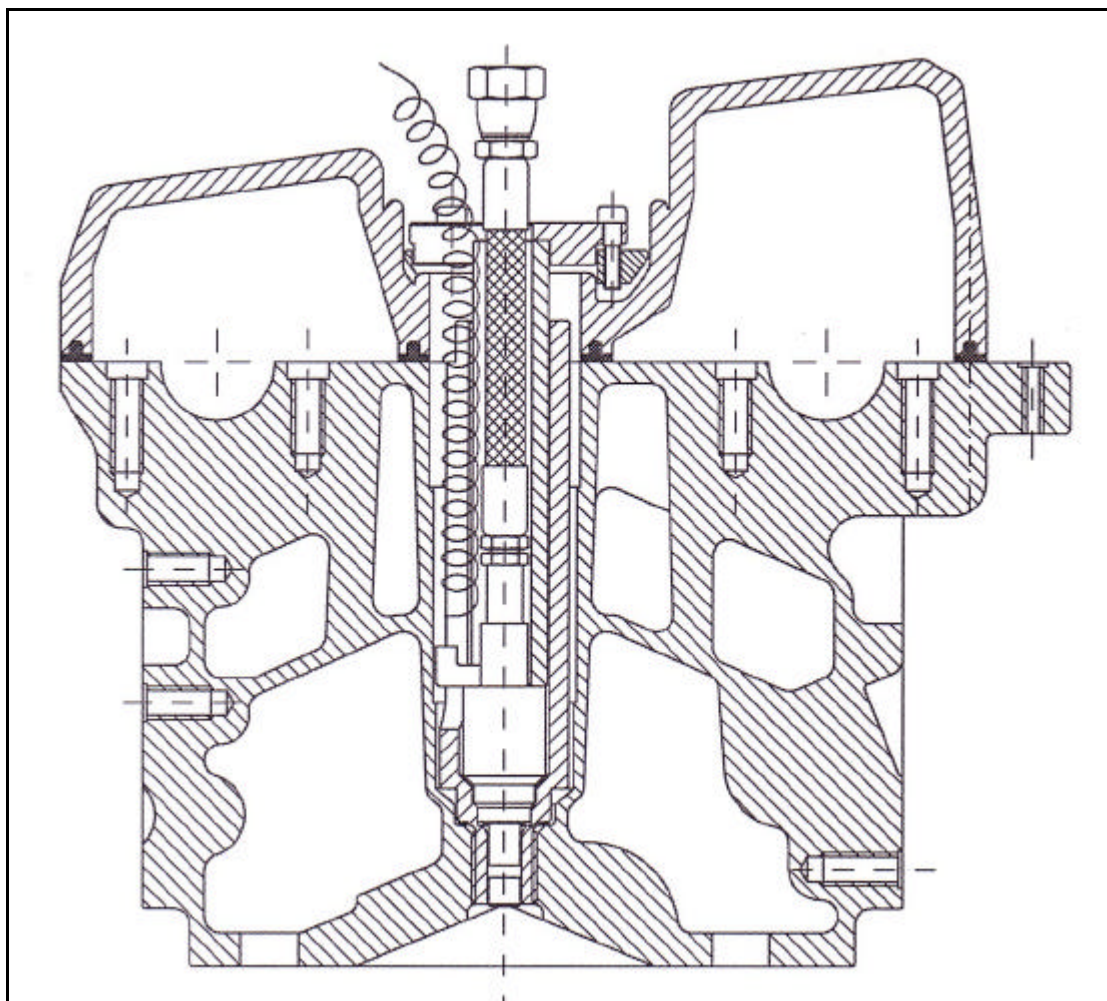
Sezione trasversale della testa con iniettore montato
